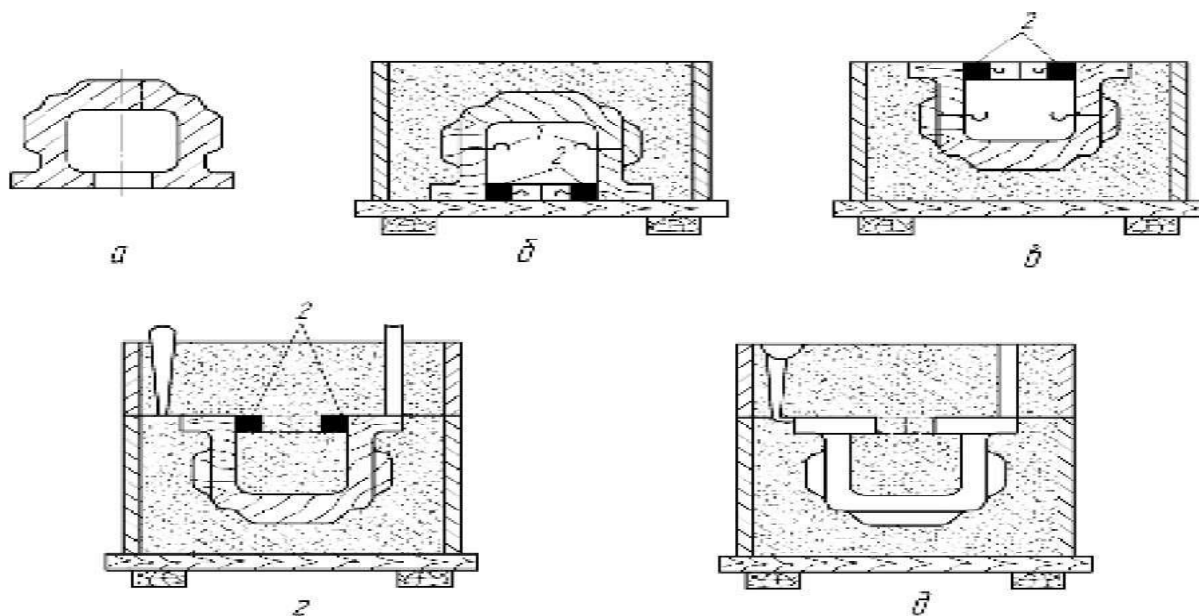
Формовка по модели с отъемными частями: *а* - деталь;
